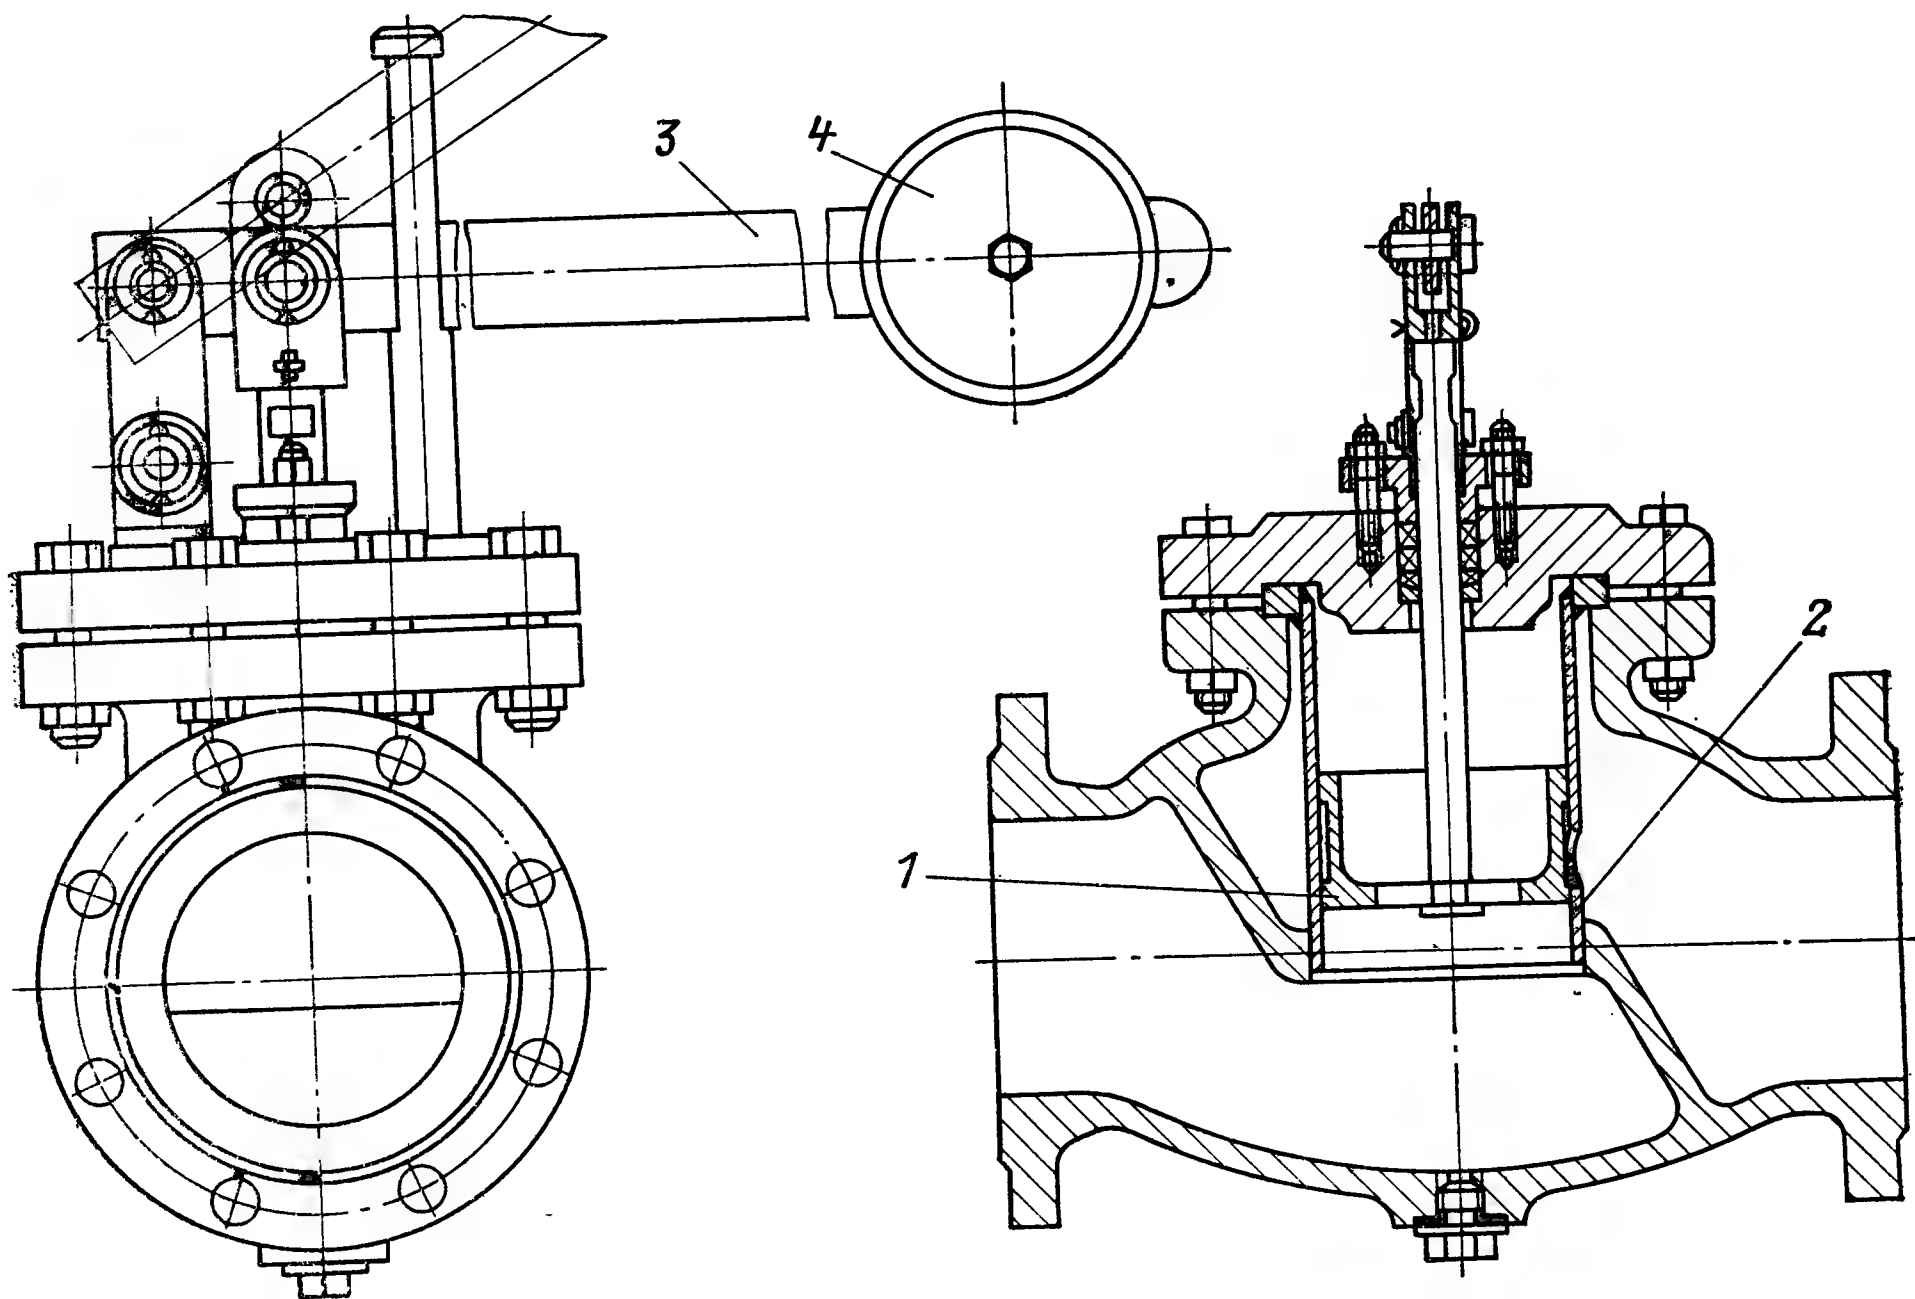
Поршневой регулирующий клапан для низких давлений.
